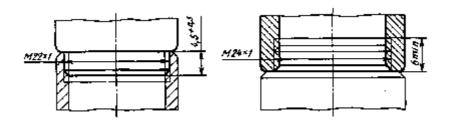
Размеры резьбы узла присоединения аэратора к изливам
